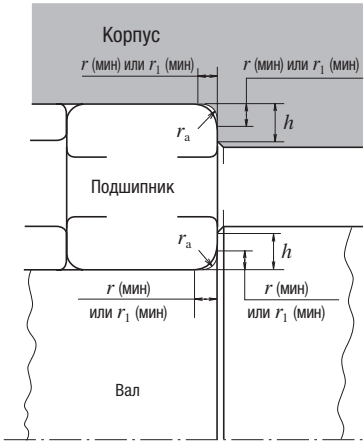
Размеры фасок, радиусы галтели вала и корпуса и высота заплечика
